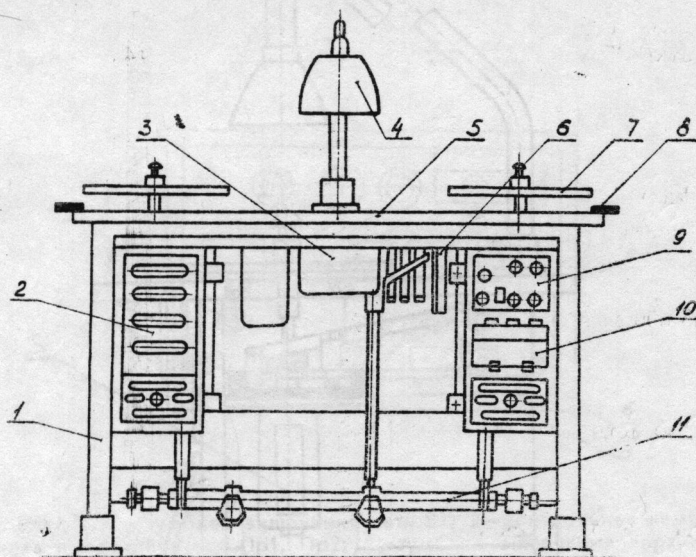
1—каркас; 2—тумбочка; 3—фонарь; 4—верхний свет; 5—столешница; 6—контактор; 7—диск; 8—щитки ограждения; 9—пульт; 10—тумбочка; 11—педальный механизм.
